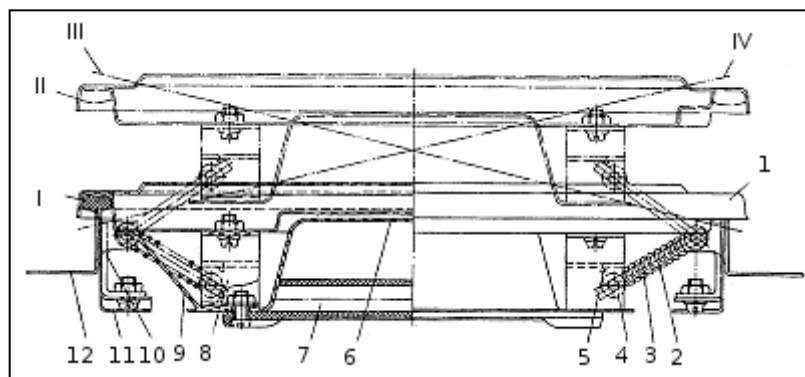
Люк вентиляционный крыши: 1 – крышка вентиляционного люка; 2 – пружина рычага; 3 – рычаг крышки люка; 4 – ролик подвижный рычага; 5 – упор рычага; 6 – облицовка люка; 7 – ручка люка; 8 – кронштейн крышки люка; 9 – козырек вентиляционного люка; 10 – кронштейн люка; 11 – усилитель вентиляционного люка; 12 – крышка кабины; I – закрытое положение крышки люка; II, III, IV – три открытых положения крышки люка
